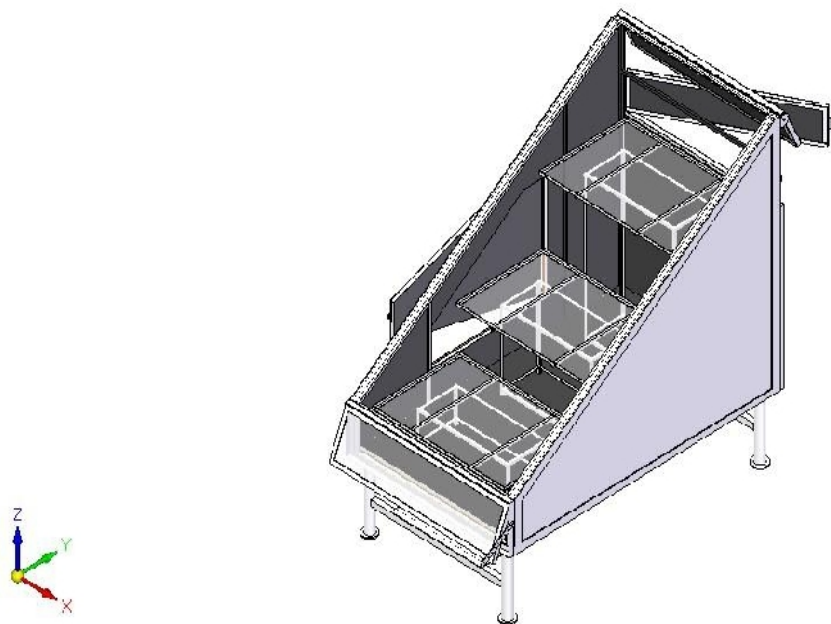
vue d'ensemble de la serre séchoir réalisée.
